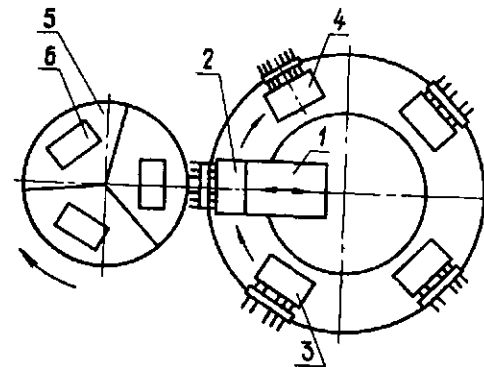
Схема переоснащения АС сменными шпиндельными коробками с помощью кольцевого стола-транспортера
